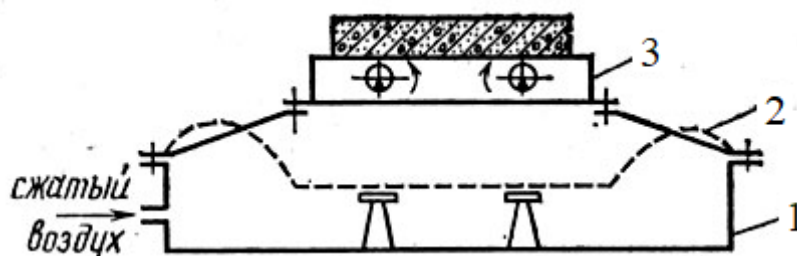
Схема пневматических виброизоляторов: 1 – камера воздушной подушки; 2 – гибкая резинокордная оболочка; 3 – виброплатформа
